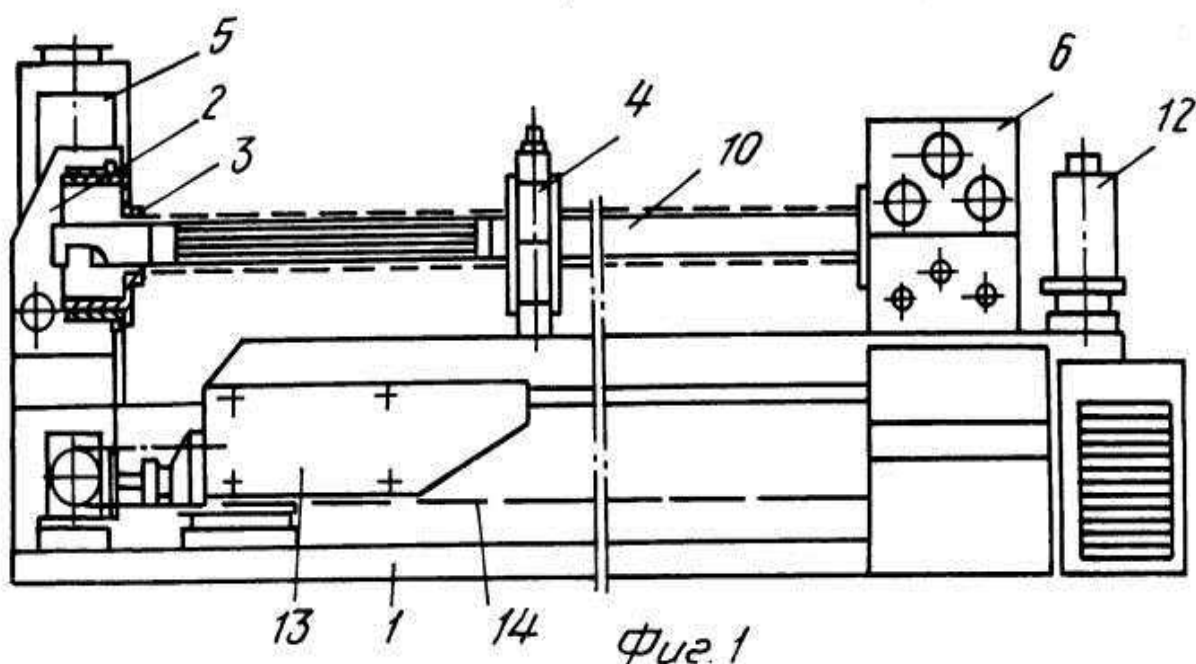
"Установка для нанесения покрытия на внутреннюю поверхность трубы" схематичное изображение.
